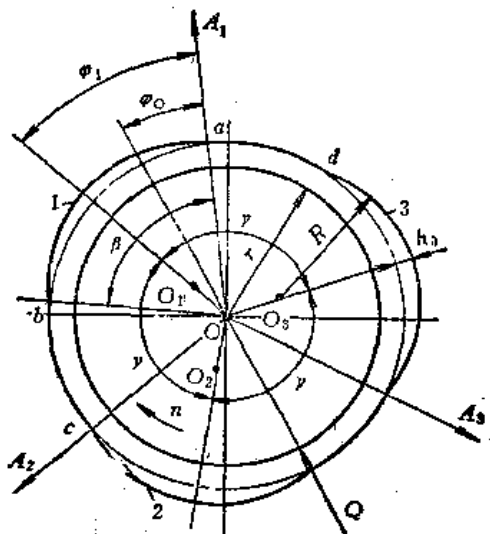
三内偏心圆弧面径向轴承结构示意图
